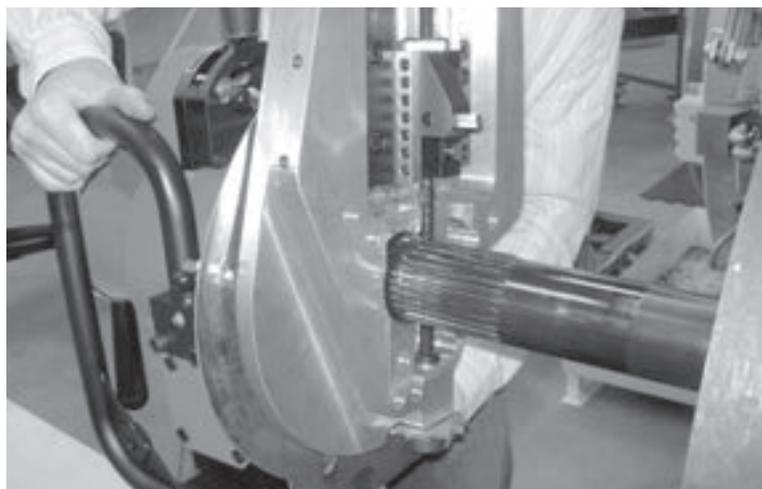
Coloque la máquina EP 424 en posición para montarla en el mandril.
